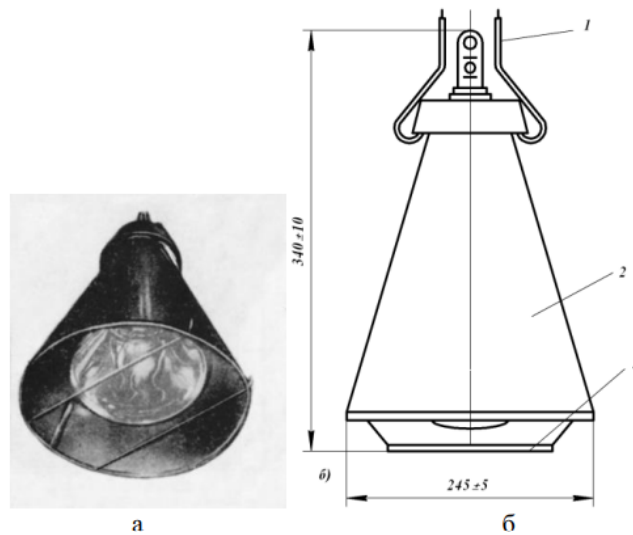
Інфрачервоний опромінювач типу ОРИ-1: а) загальний вигляд; б) схема конструкції: 1 – підвіска; 2 – корпус; 3 – сітка
